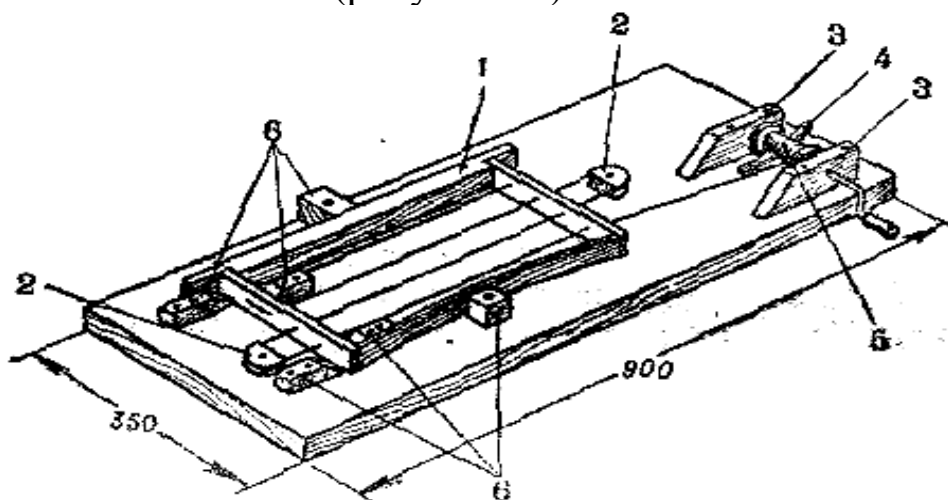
Станок для натягивания проволоки: 1 - рамка; 2 - направляющие полукруги; 3 - колодочка для установки валика с катушкой; 4 - притормаживающая плоская пружина; 5 - катушка с проволокой; 6 - зажимы
